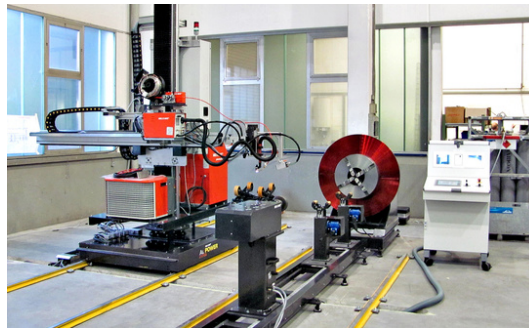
Sistema automático para soldadura circunferencial de tubos de pequeno diâmetro [47]
